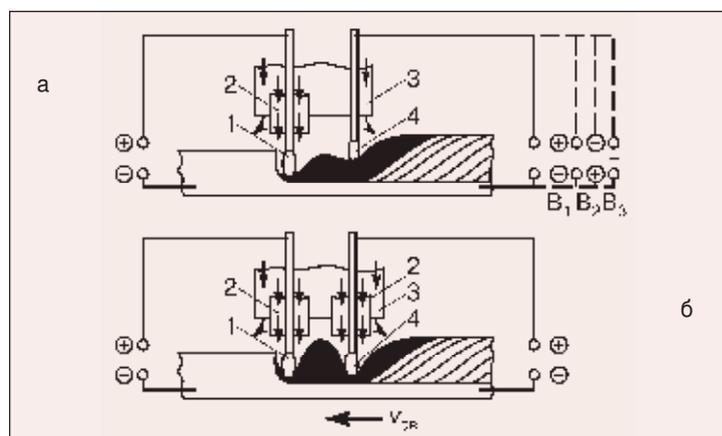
Схема двухдуговой сварки с двухскоростной газовой защитой одной (а) и двух (б) дуг: 1, 4 — соответственно первая и вторая дуга; 2 — сопло для подачи высокоскоростного потока газа; 3 — сопло для подачи защитного газа с обычной скоростью
